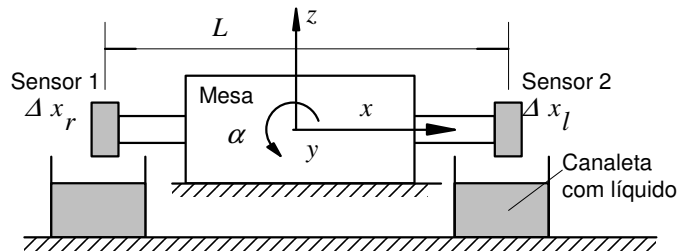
Montagem para a medição do ângulo roll, com o uso de duas superfícies de líquido
